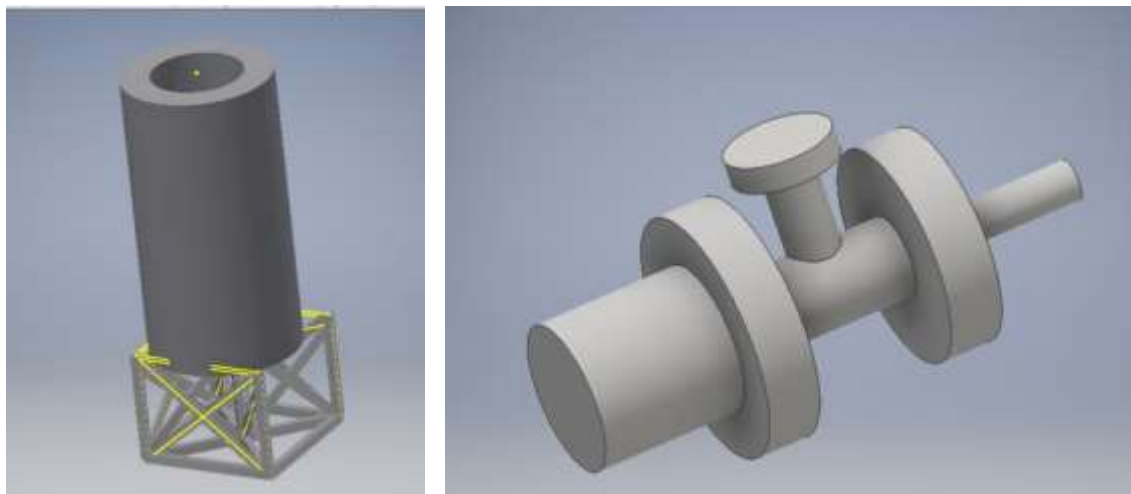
Сборка рамы и корпуса (а) и форсунка топливная (б)
